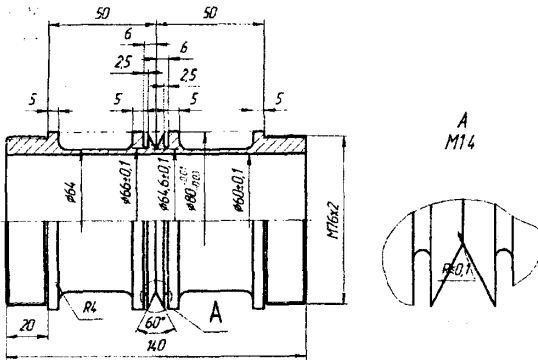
Конструкція зразка індикатора різьбового з'єднання 3-121 для випробування на опір втомі
